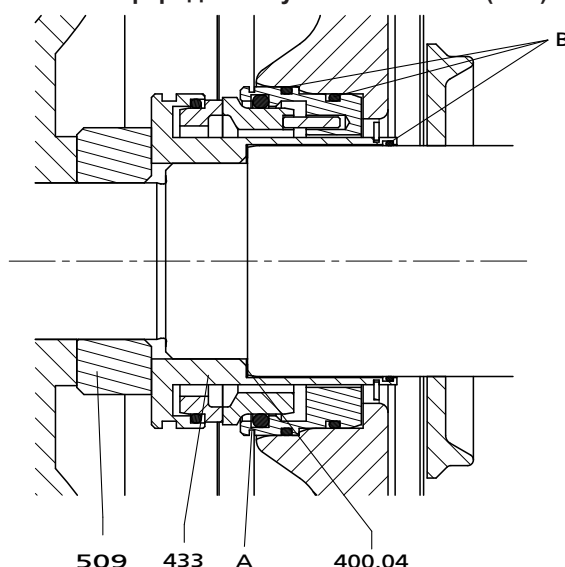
Монтаж уплотнительного блока KSB (4EB)
